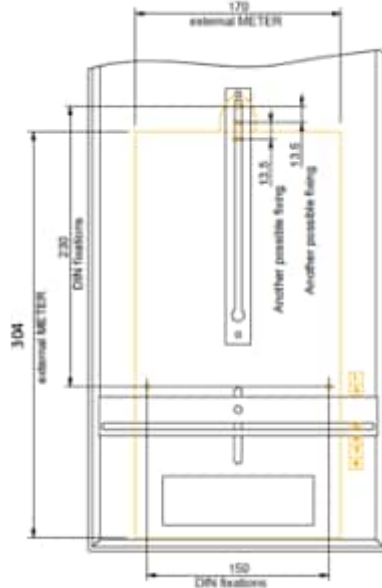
Installationsdreieck-Ansicht (Standard-Klemmendeckel)
